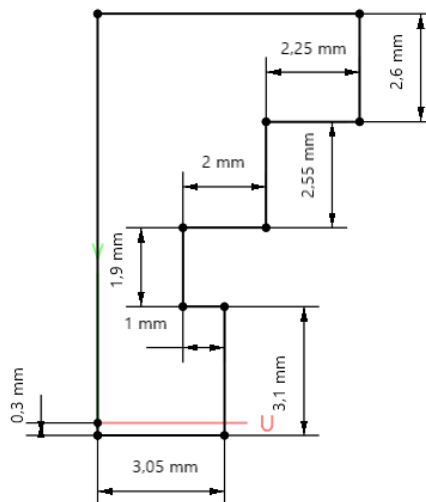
Dimensiones geométricas empleadas para el diseño del segundo tipo de soporte para la pieza 7.
